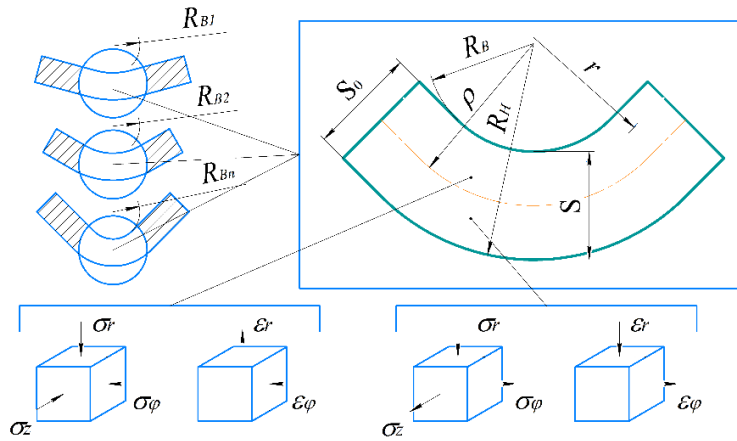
Схема напружено-деформованого стану при гнутті заготовки; S_0 – початкова товщина заготовки; S – поточна товщина; r – поточний радіус;
